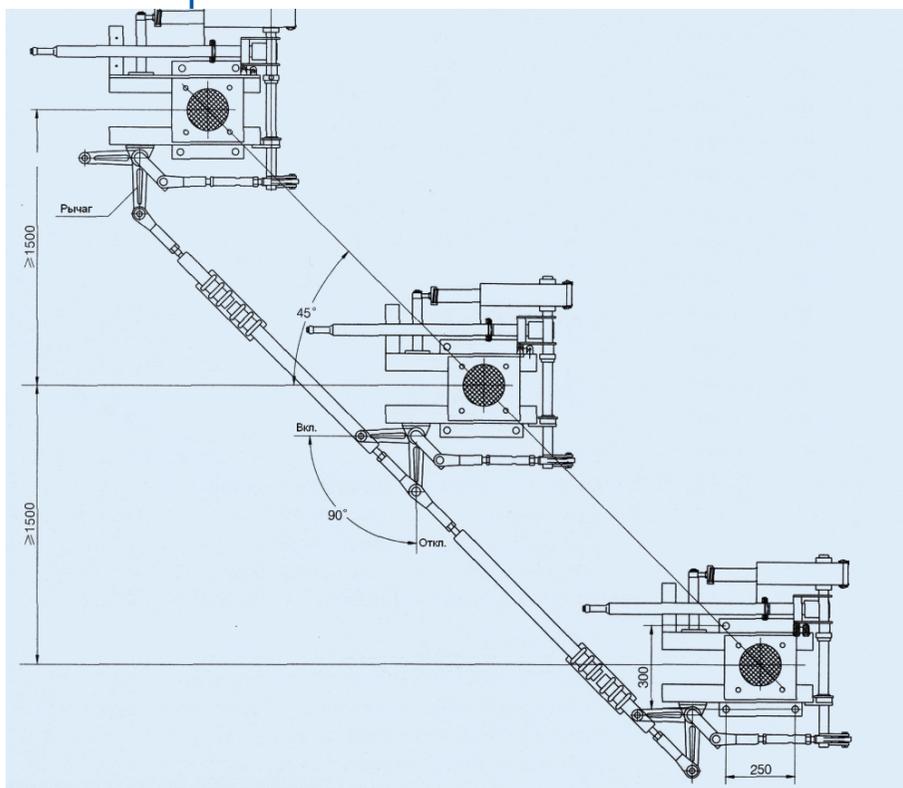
Внешний вид и размеры заземлителя JW□-126
